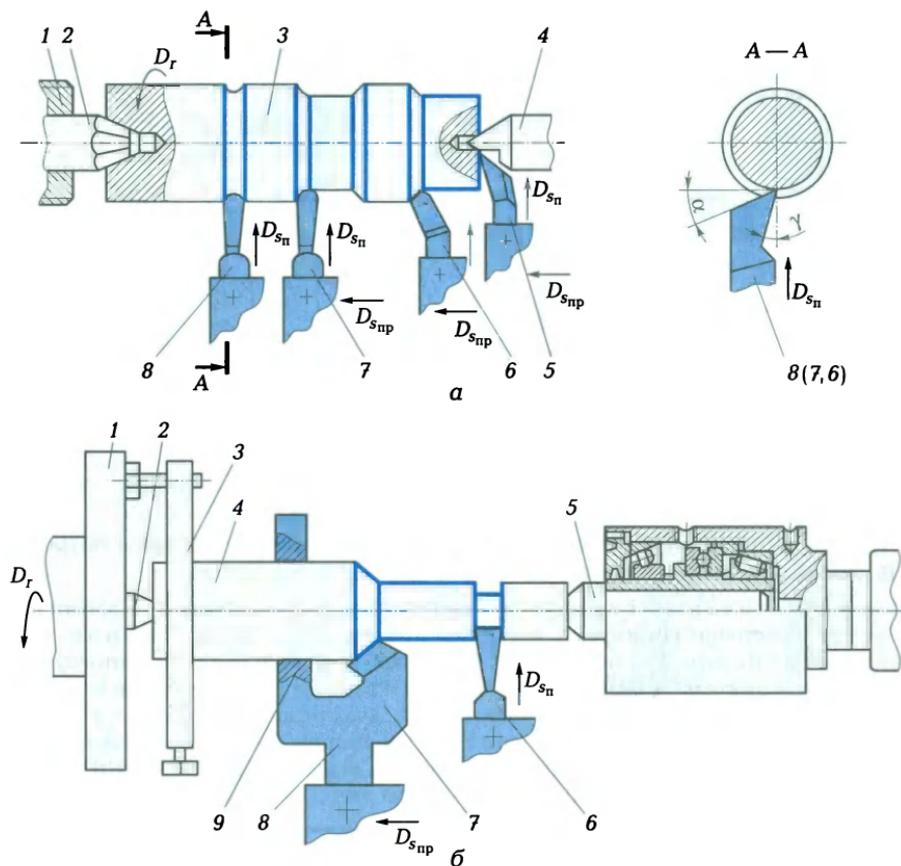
Схемы обработки заготовок, закрепленных в опорных, рифленых и вращающихся центрах:
